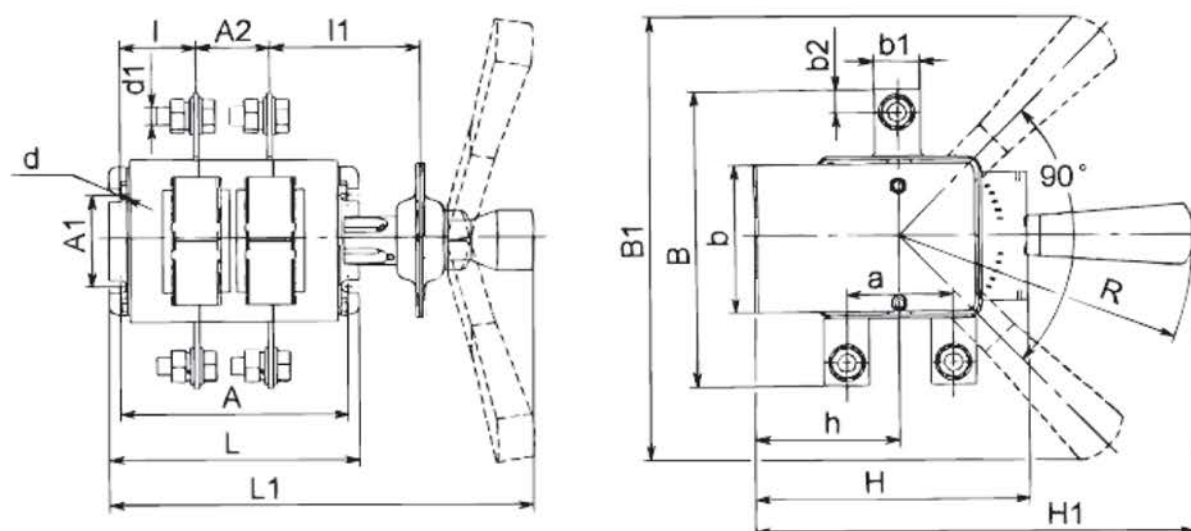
Выключатель-разъединитель двухполюсный на одно направление с передней смещенной рукояткой.
